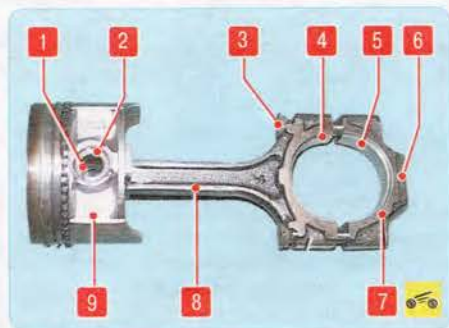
Шатунно-поршневая группа: 1 – стопорное кольцо; 2 – поршневой палец; 3 – выступ на шатуне; 4, 5 – вкладыши; 6 – уступ на крышке шатуна; 7 – крышка шатуна; 8 – шатун; 9 – поршень
